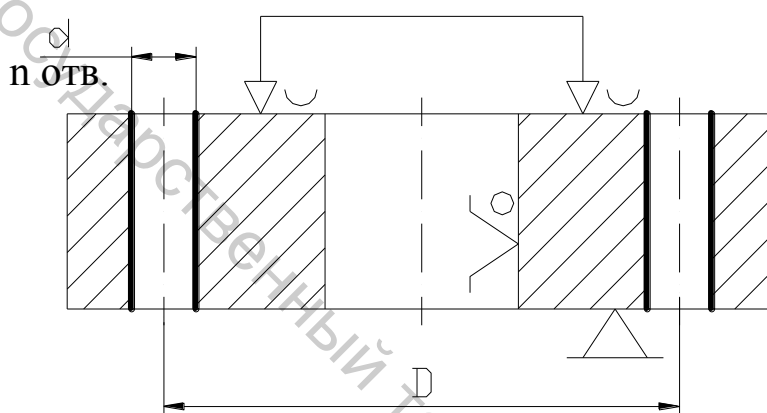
Схема установки заготовки на плоскость и цилиндрический палец
